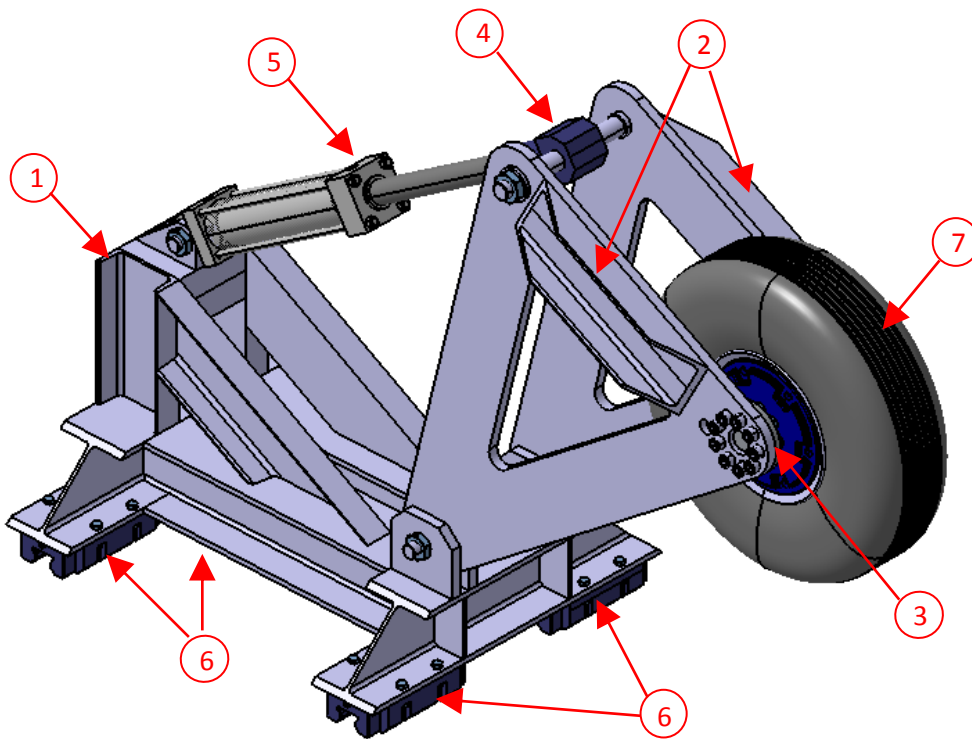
Esquema constructivo del conjunto carro porta rueda.
